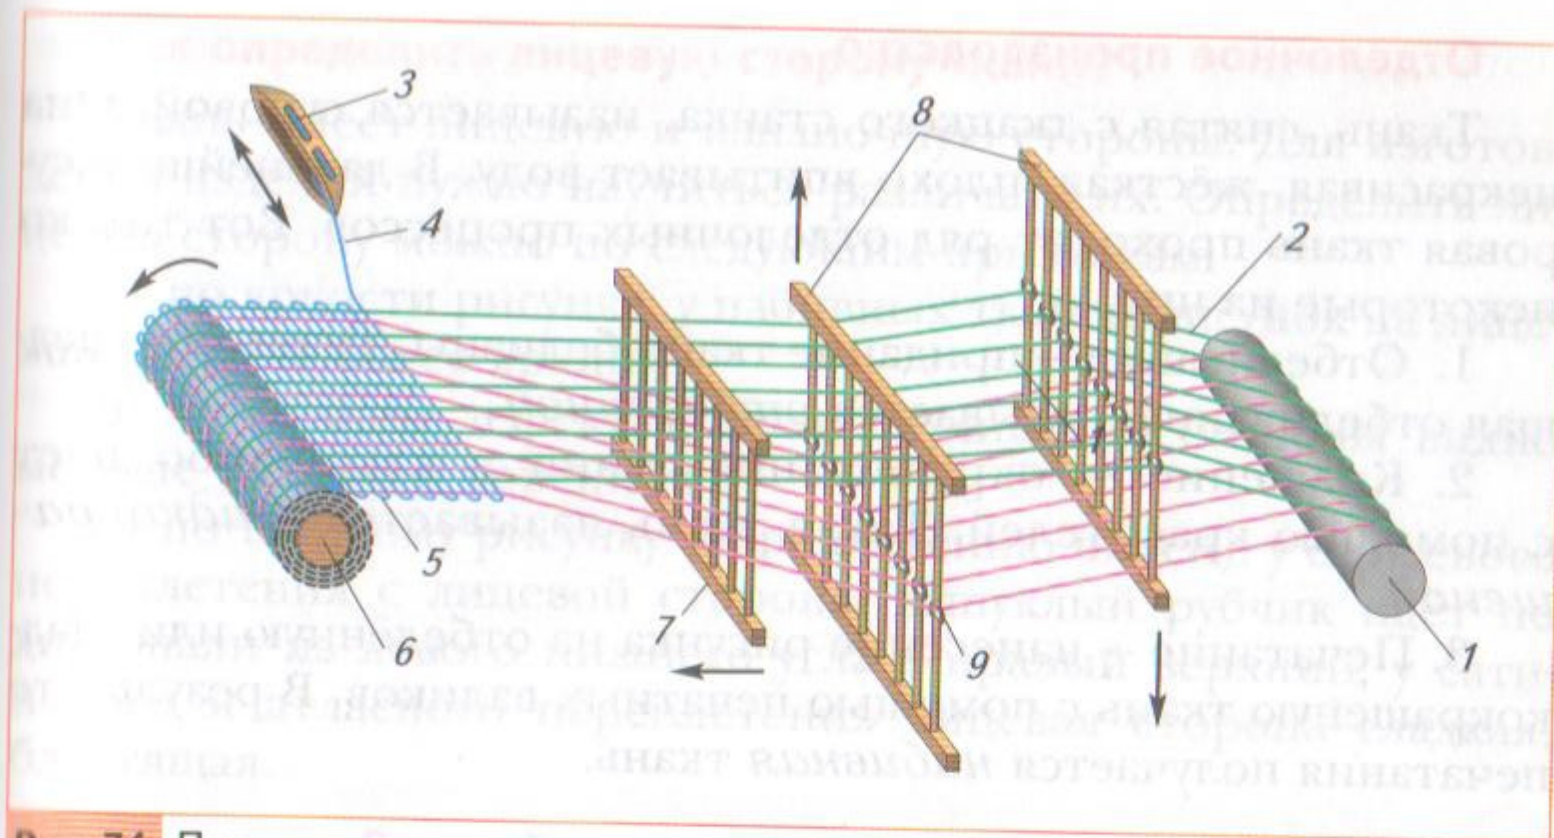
Процесс изготовления ткани на ткацком станке: 1 — навой; 2 — нити основы; 3 — челнок; 4 — нити утка; 5 — кромка; 6 — товарный валик; 7 — бердо; 8 — ремизки; 9 — глазок ремизки
